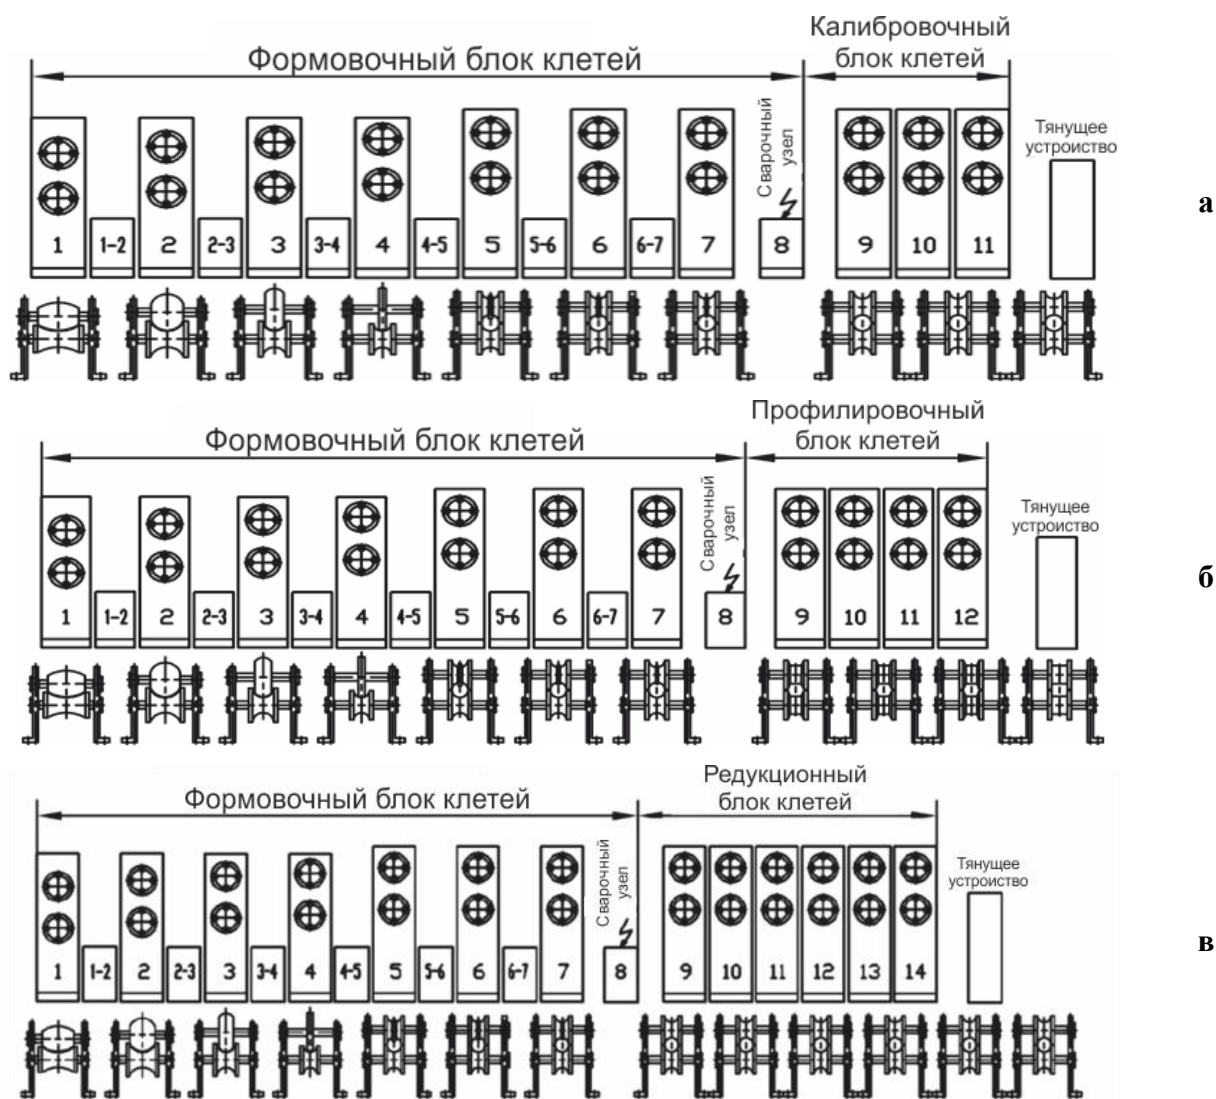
Основные производственные компоновки: а) компоновка клеток для получения сварных труб круглого сечения; б) компоновка клеток для получения сварных профилированных труб из круглой заготовки; в) компоновка клеток для получения сварных холодно-редуцированных труб
